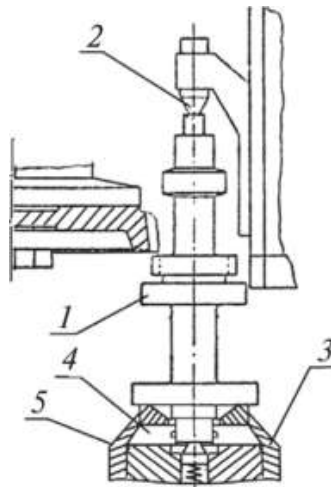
Схема пристрою для обробки циліндричних валів-шестерень на зубодолбіжному верстаті
